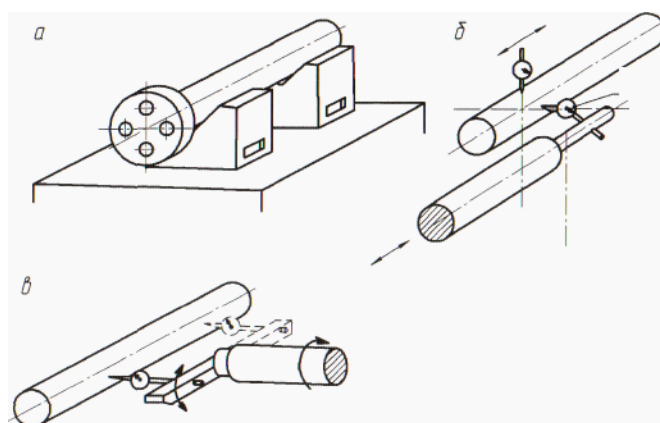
Установка (а) и выверка (б, в) заготовок на призмах
